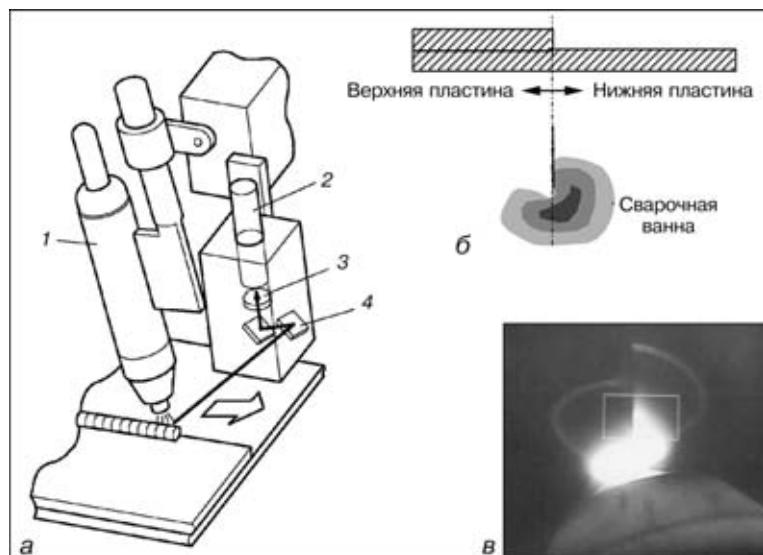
Расположение датчика и обработка изображения: *а* — расположение сварочной горелки и датчика (1 — плазменная горелка; 2 — видеокамера; 3 — фильтр; 4 — зеркало); *б* — обработка изображения для распознавания линии сварки; *в* — изображение, полученное с помощью видеокамеры
